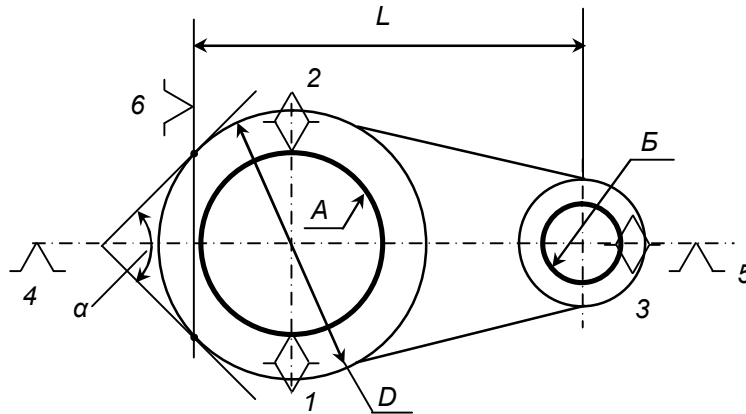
Сема базування заготовки деталі типу «Важіль»
